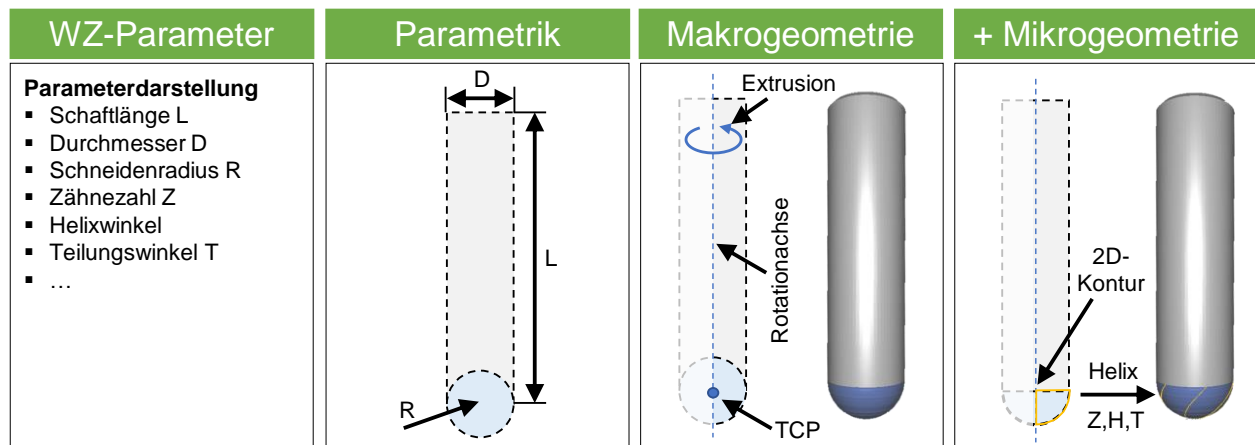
Generator-Modul zur Ableitung von Werkzeugmakro- und Werkzeugmikrogeometrie
